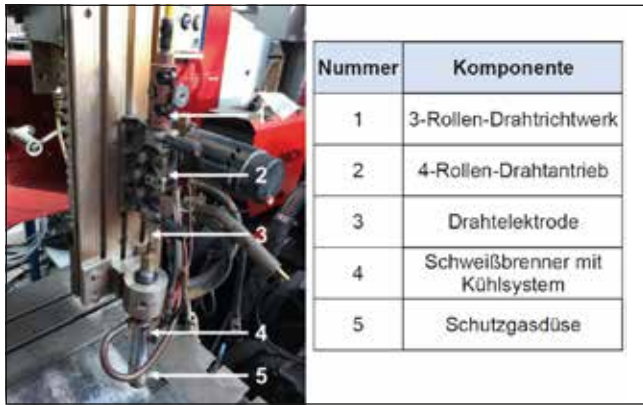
• Versuchsstand (links) und Bezeichnung der Komponenten (rechts).
